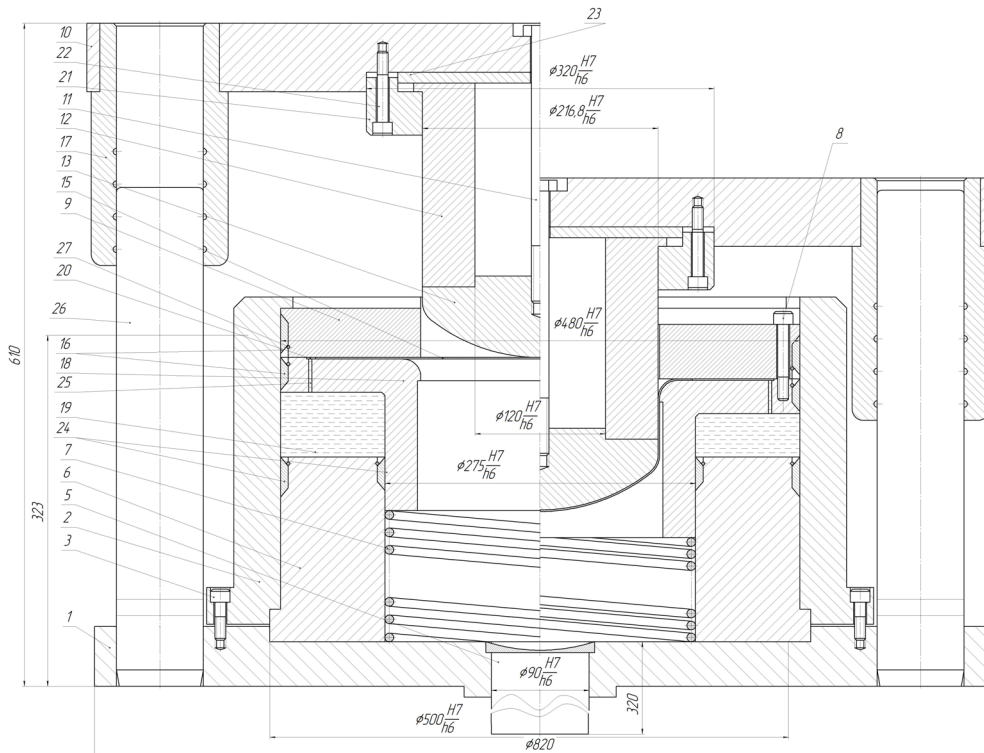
Конструкція штампу для витягування з диференційованим радіальним підпором фланця заготовки
